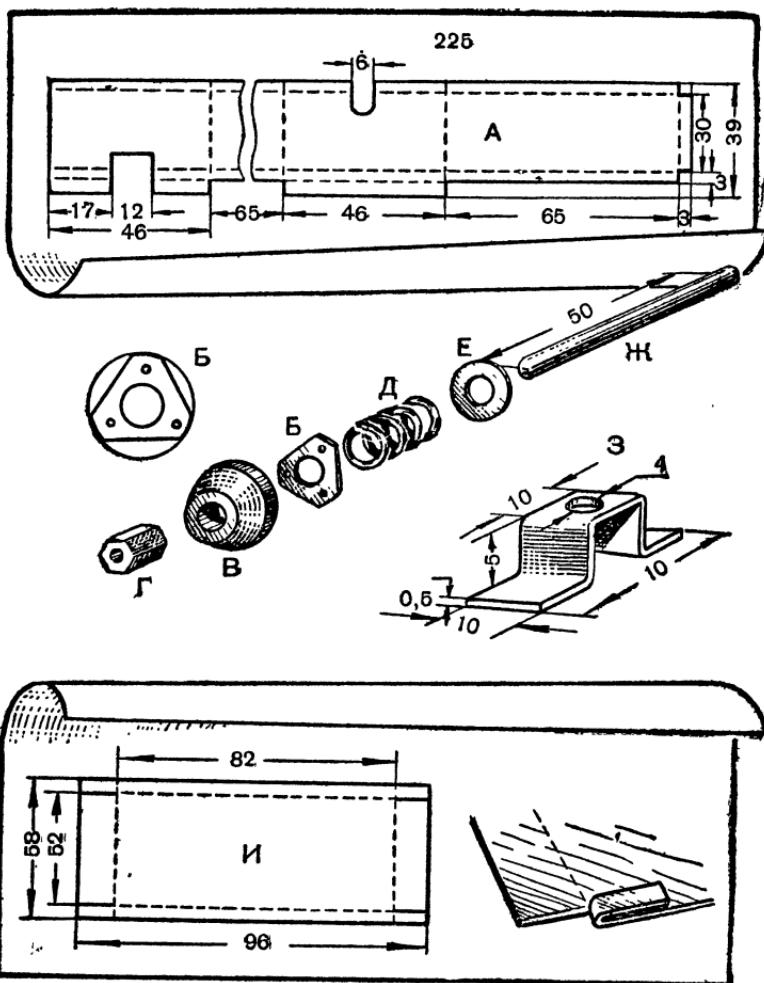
Детали редуктора № 5 (рис. 117): А — развертка боковой стенки корпуса; Б — жестяная накладка, В — малый фрикцион из щечки от катушки; Г — обрезок карандаша; Д — спиральная пружина; Е — шайба; Ж — вал малого фрикциона; З — нижний подшипник; И — развертка дна корпуса.
